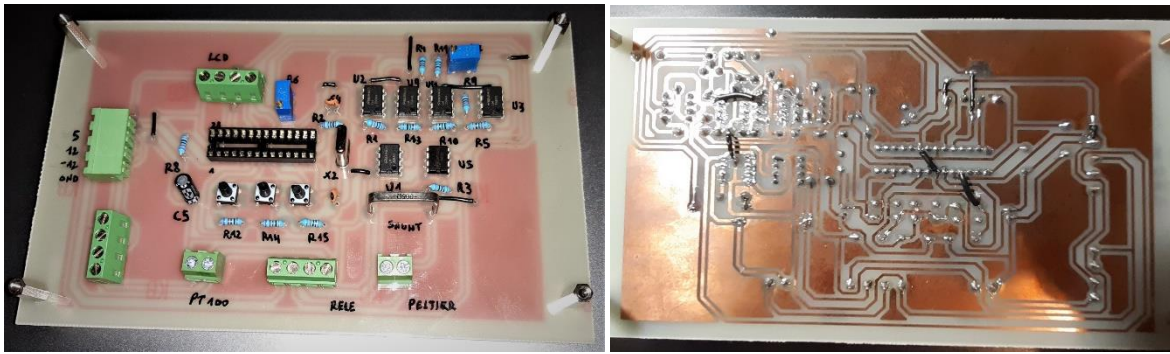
PCB sistema de refrigeración mediante célula Peltier.
